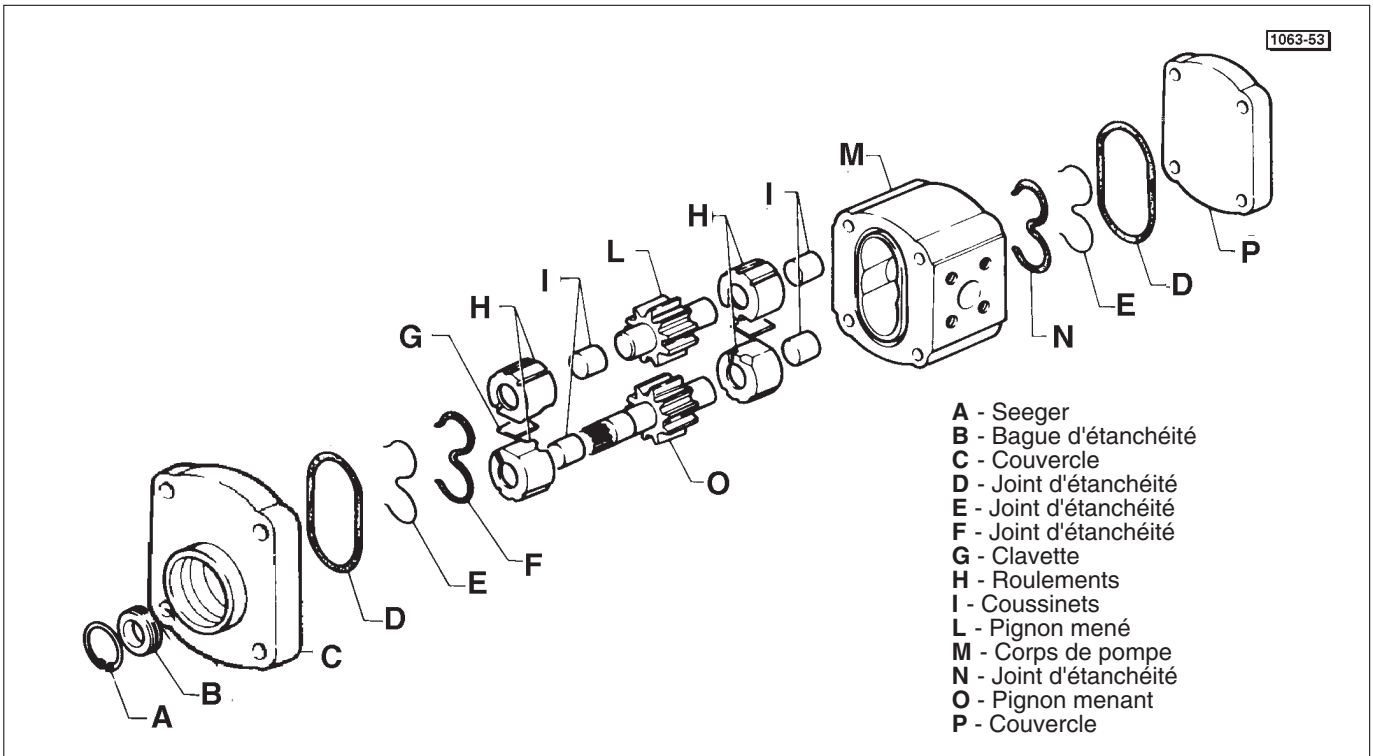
Éléments constitutifs de la pompe hydraulique.
